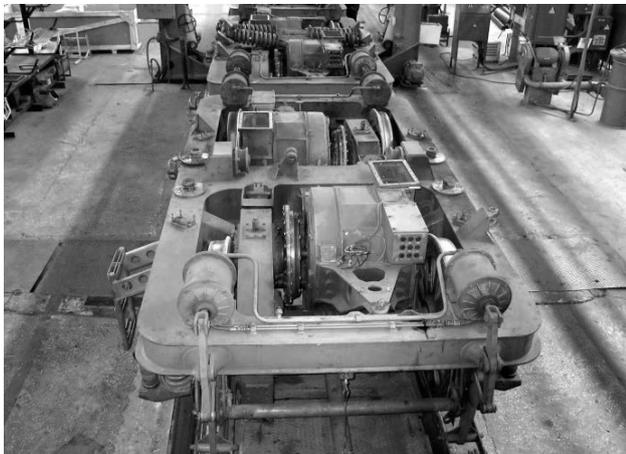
Внешний вид тягового двигателя в составе тележки электровоза
